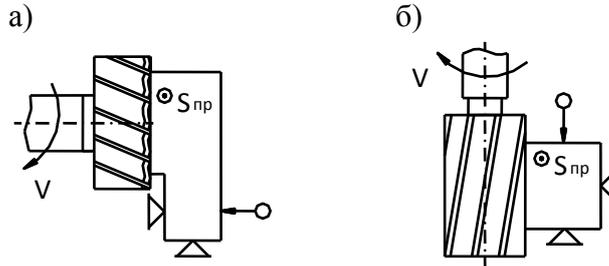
Схемы фрезерования вертикальных поверхностей.
